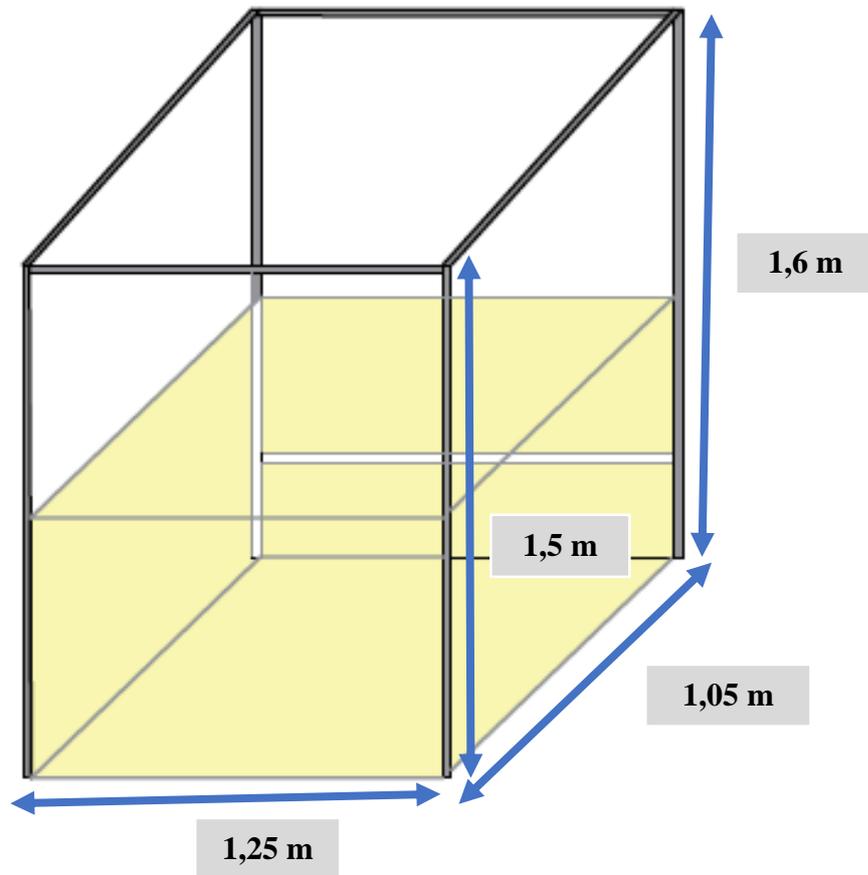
Estructura para el soporte de la cubierta. Medidas exteriores.
